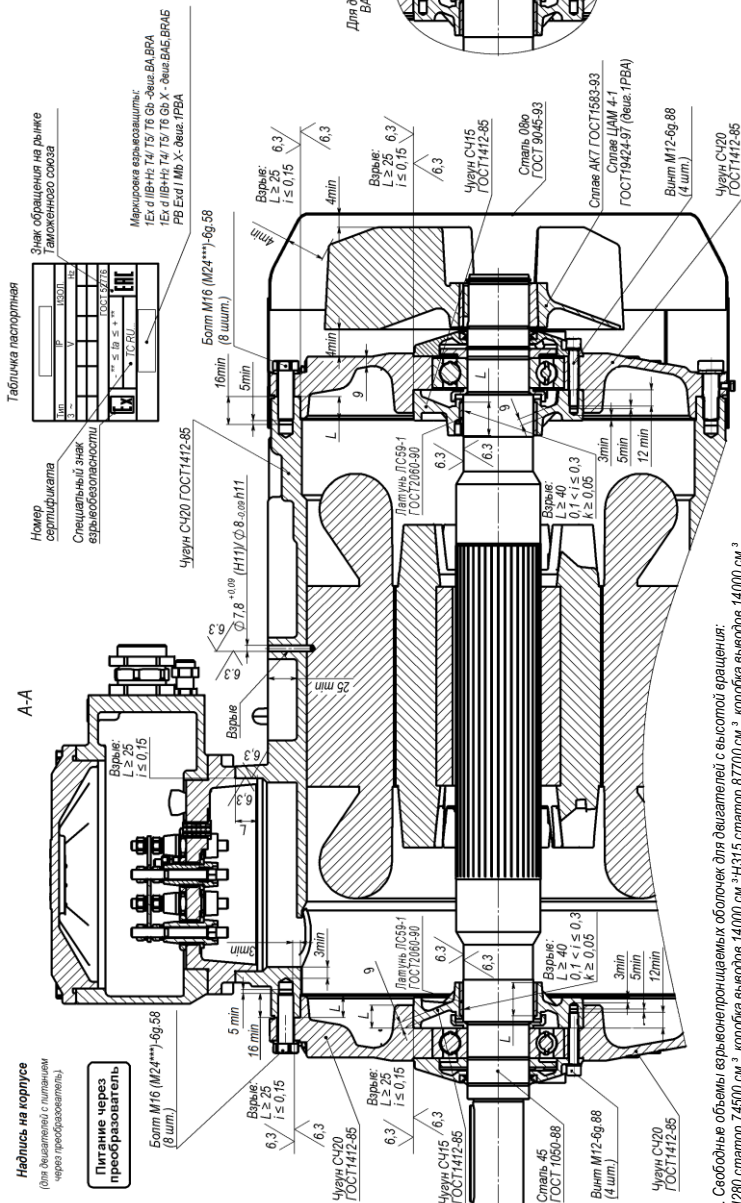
Чертеж взрывозащиты коробки выводов «d» двигателей ВА(Б),1РВА 250,280; ВРА(Б),1РВРА 280,315
